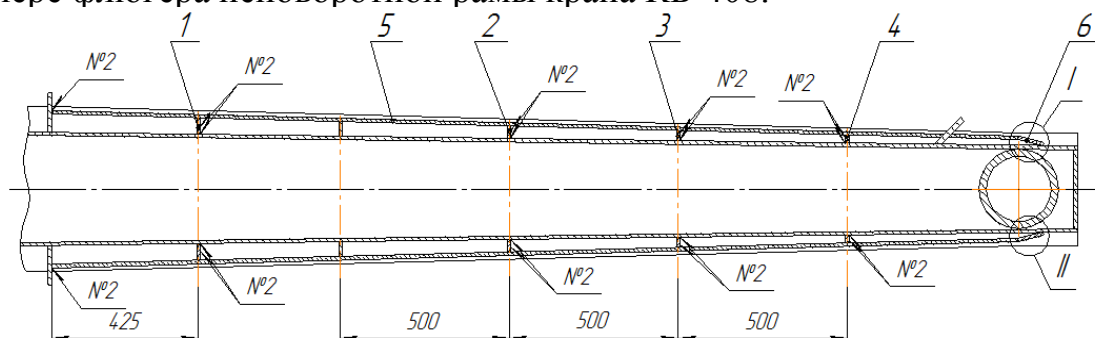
Усиление металлоконструкции флюгера неповоротной рамы крана КБ-408
